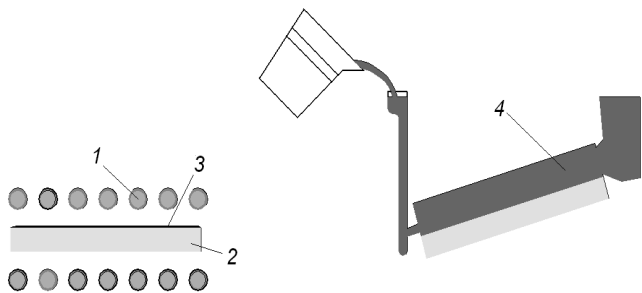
Схема процесса заливки жидкого металла на твердую заготовку [7]: 1 – индуктор; 2 – стальная заготовка; 3 – защитный флюс; 4 – износостойкий чугун
